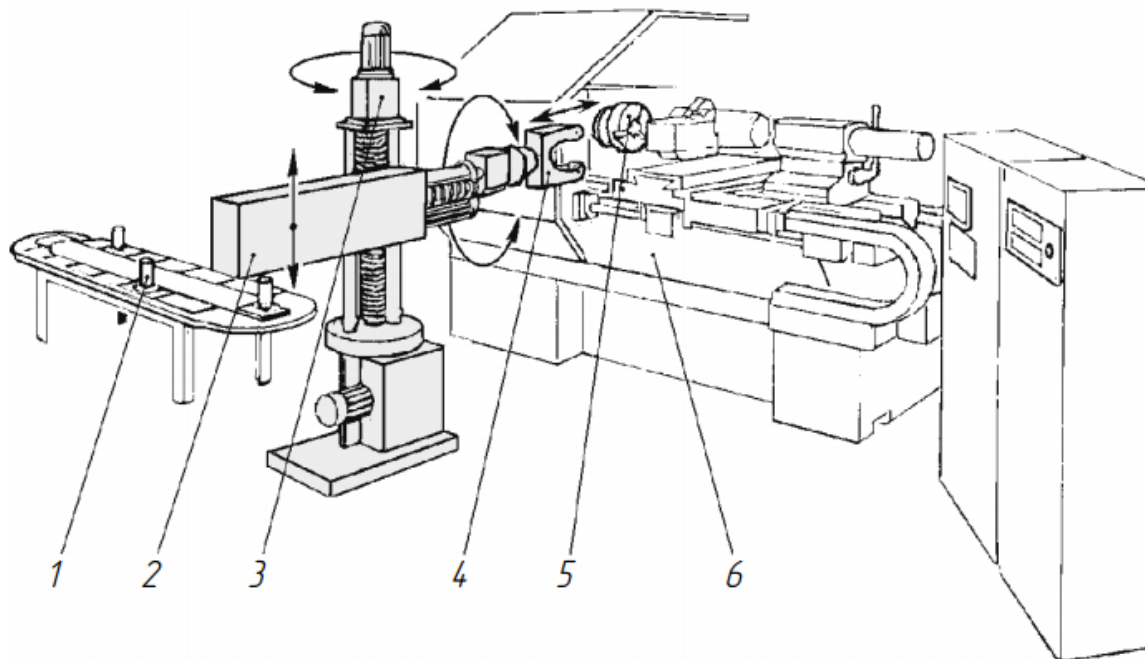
ГПМ со станком 16К20ФЗР и роботом напольного типа М20П.40.01: 1 — заготовки; 2 — механизм продольного перемещения схвата робота; 3 — механизм вертикального перемещения схвата робота; 4 — схват; 5 — патрон; 6 — станок.
